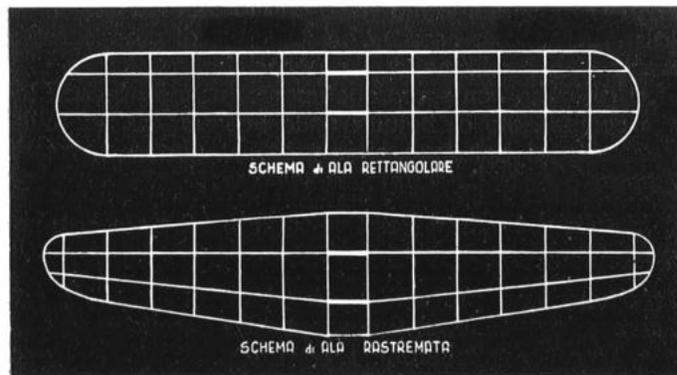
Ala a pianta rettangolare ed a pianta rastremata.
